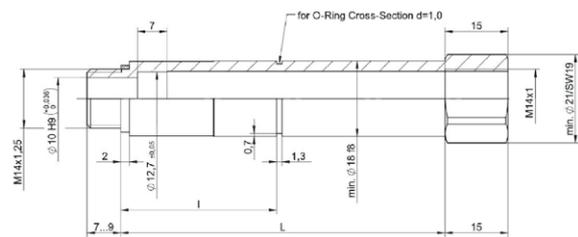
Einbau mit Montagehülse Typ 6586AQ
